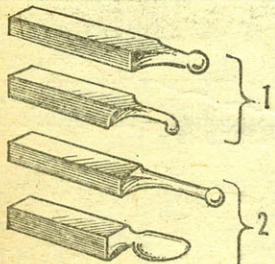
Давилники: 1 — основные, 2 — для формовки канавок.
